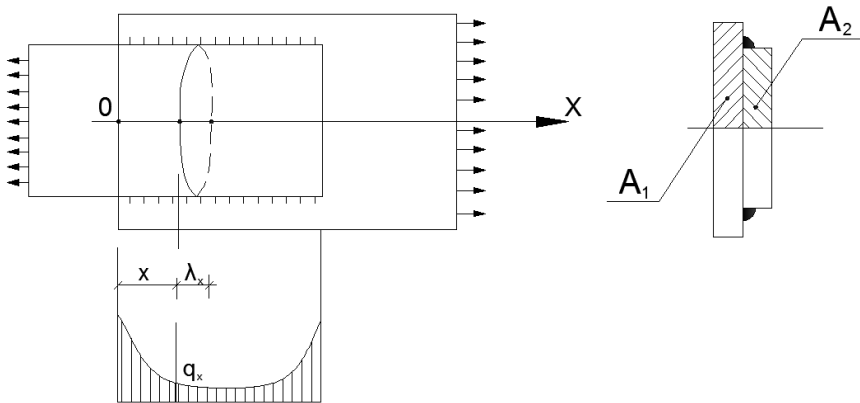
Расчетная схема сварного соединения с фланговыми швами [38; 39]
